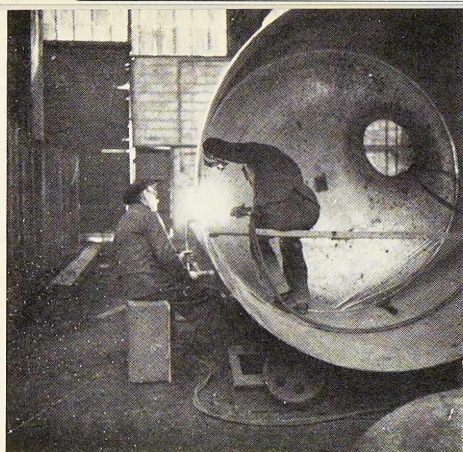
à 6 (de gauche à droite). - Construction de chaudronnerie soudée au chalumeau à deux opérateurs. - Tôle de dennebord raidie transversalement par des cornières soudées en atelier de préfabrication d'un gouvernail
